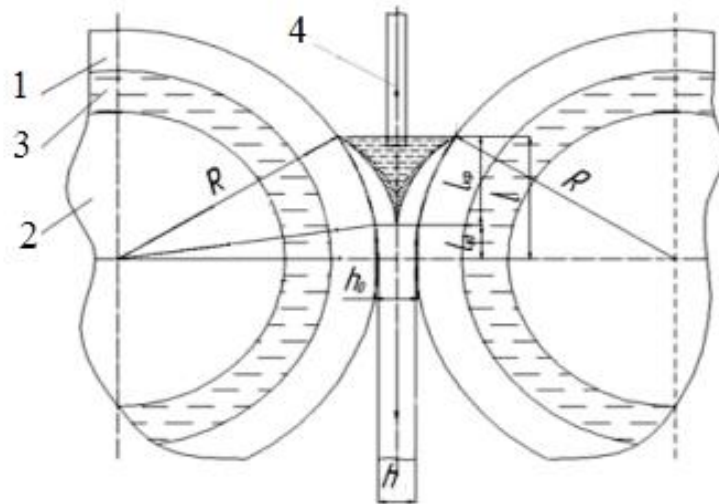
Схема процесу валкового розливу-прокатки (без додаткового деформуючого інструмента): 1 – бандаж валка-кристалізатора; 2 – ось валка-кристалізатора; 3 – охолоджуюча рідина; 4 – сопло; R – радіус валка-кристалізатора; l – довжина ванни розплаву; $l_{кр}$ – довжина зони кристалізації; l_d – довжина зони деформації; h_0 – товщина штаби на початку зони деформації; h – товщина штаби на виході з валків [84]
